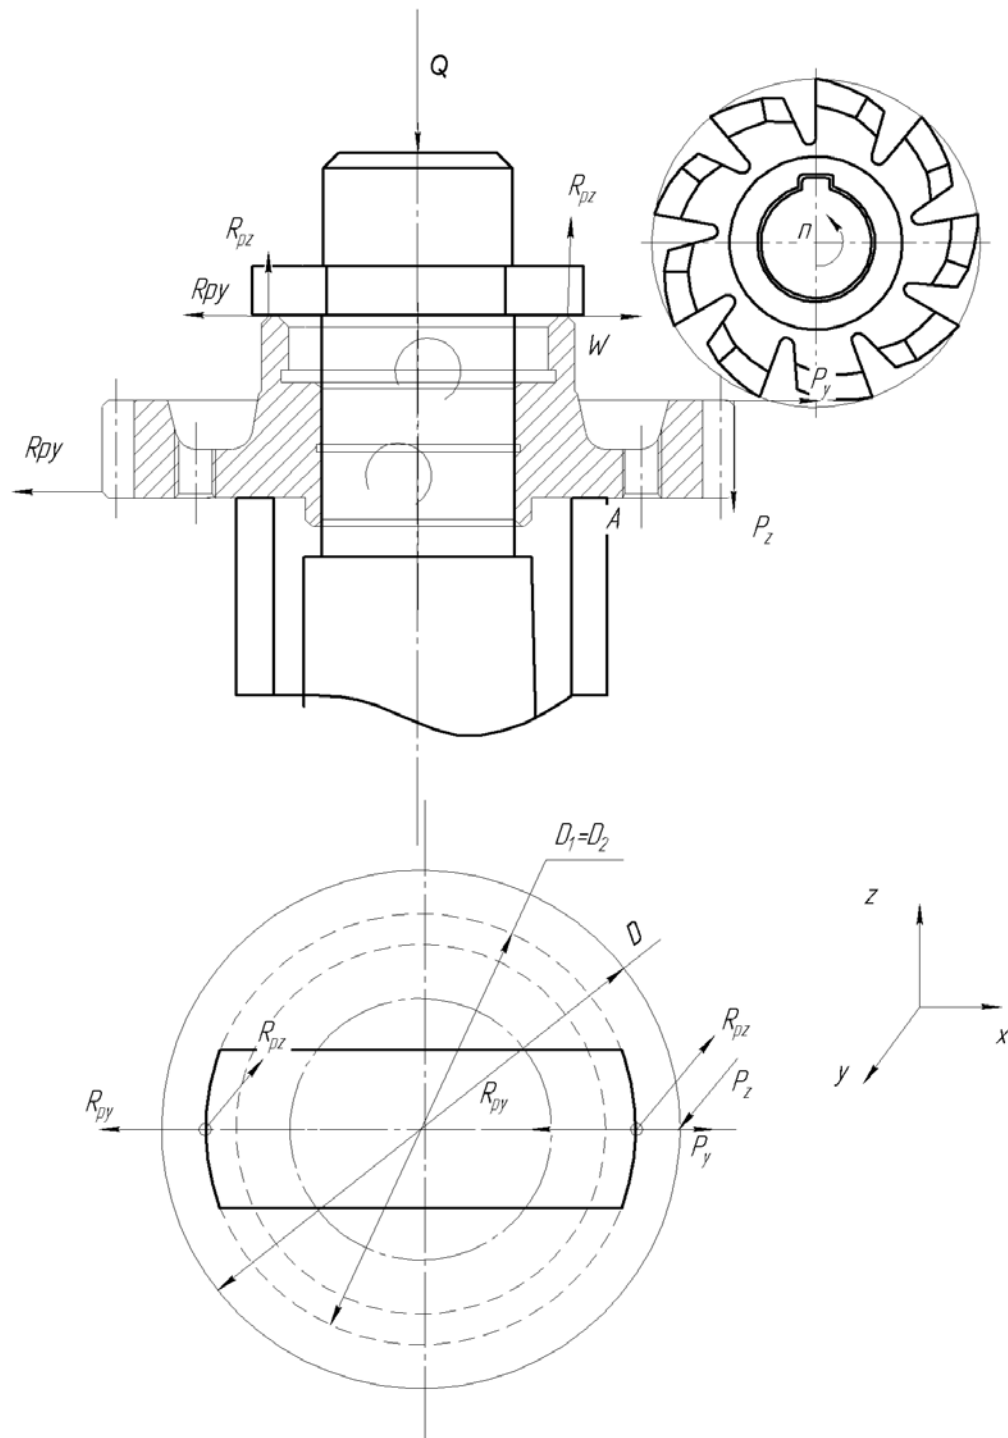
Схема дії сил на колесо зубчасте НПО 639.00.004 при обробці зубів  $m=3,5$ ;  $z=17$  на зубофрезерному верстаті з ЧПУ КТ-650 4.
